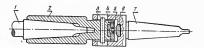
Качающаяся оправка для установки развертки: 1 — развертка; 2 — качающаяся оправка; 3 — штафт; 4 — корпус оправки; 5 — вакаленный шарик; 6 — подвятик; 7 — конический квостовик корпуса оправки;
